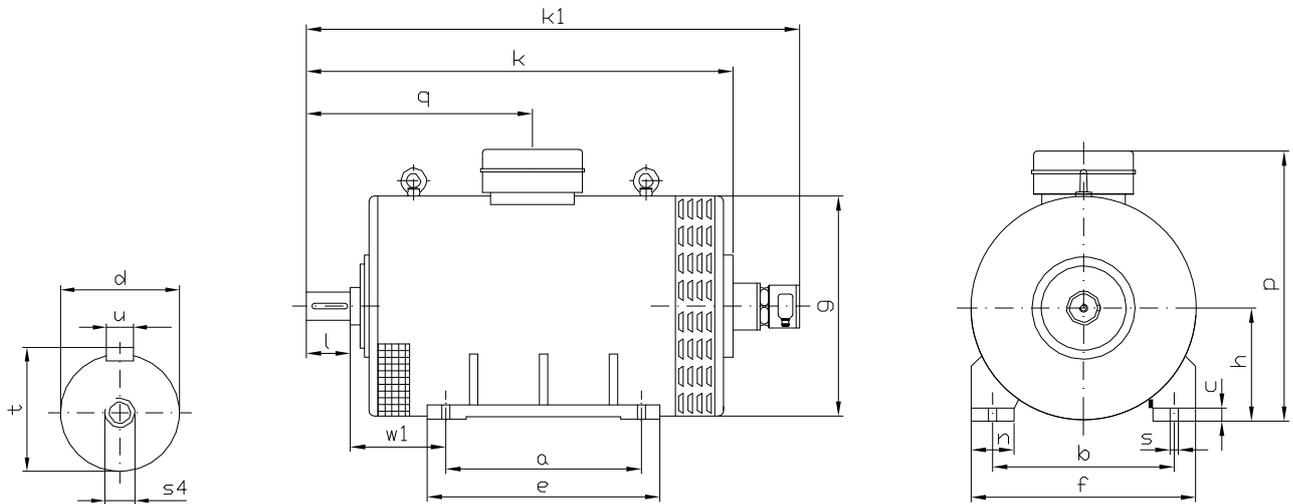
Drehstrom-Käfigläufermotor mit Encoder mit Anbauflansch: Kühlung IC 01, Schutzart: IP 23, Bauform: IM B3
